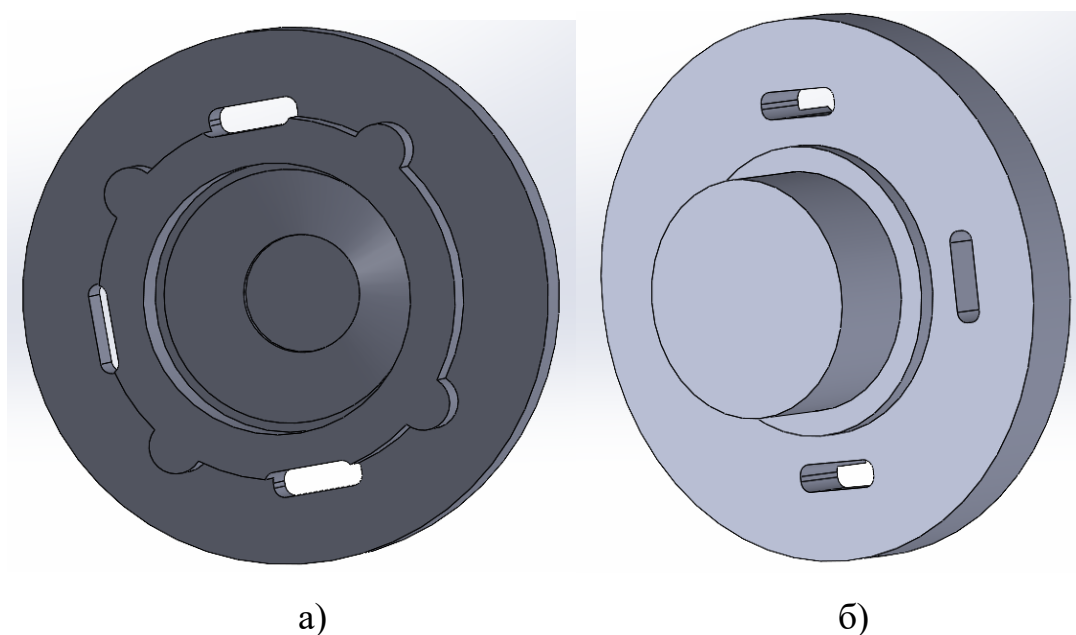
Зовнішній вигляд тривимірної моделі заготовки під лиття: вид спереду (а), вид с заду (б)
